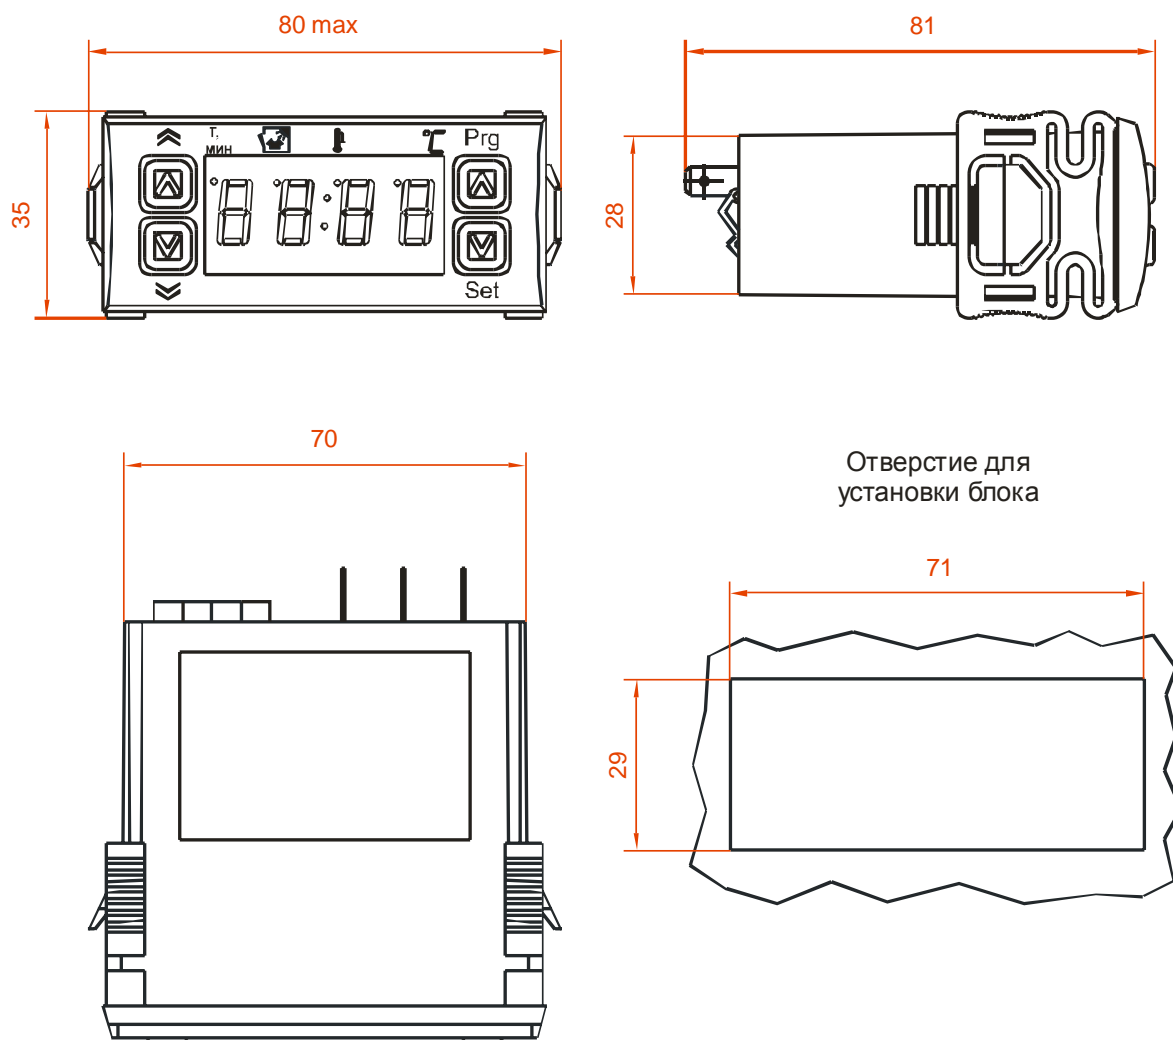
Внешний вид, габаритные и установочные размеры блока.
